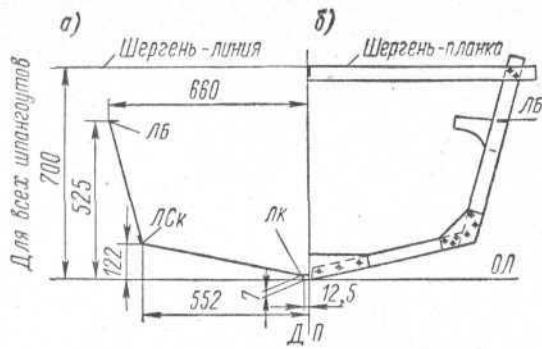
Схема разметки и сборки 3-го шпангоута: а — разметка на плазе по таблице ординат (см. табл. 17); б — сборка шпангоута с шергень-планкой.
